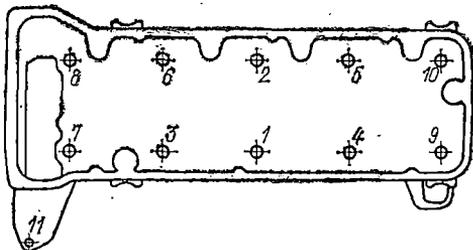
Порядок затяжки болтов крепления головки блока
